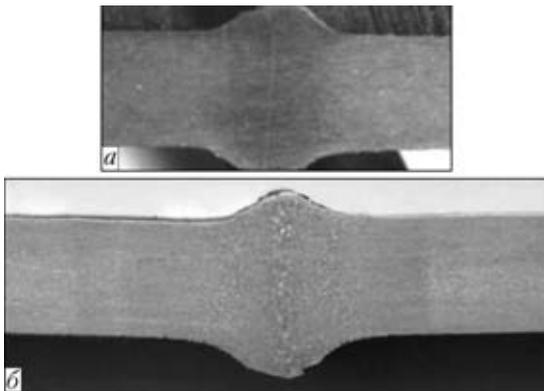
Макрошлифы сварных соединений стали X70, выполненных ПСМД (а) и КССО (б)
